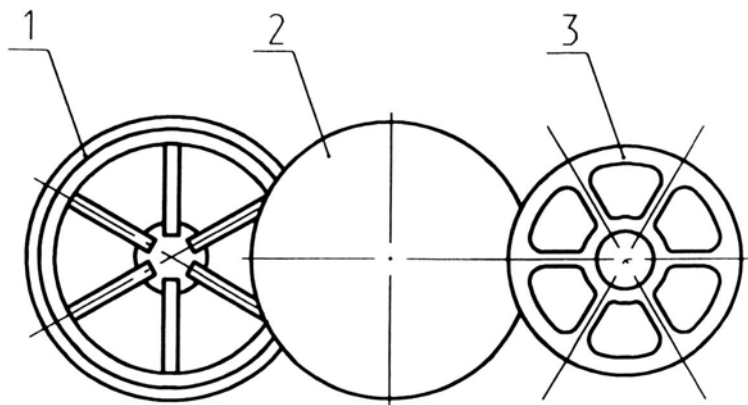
Порядок разборки и сборки встроенного фильтра: 1 – корпус входной крышки; 2 – фильтрующий элемент; 3 – кольцо крепления фильтра
